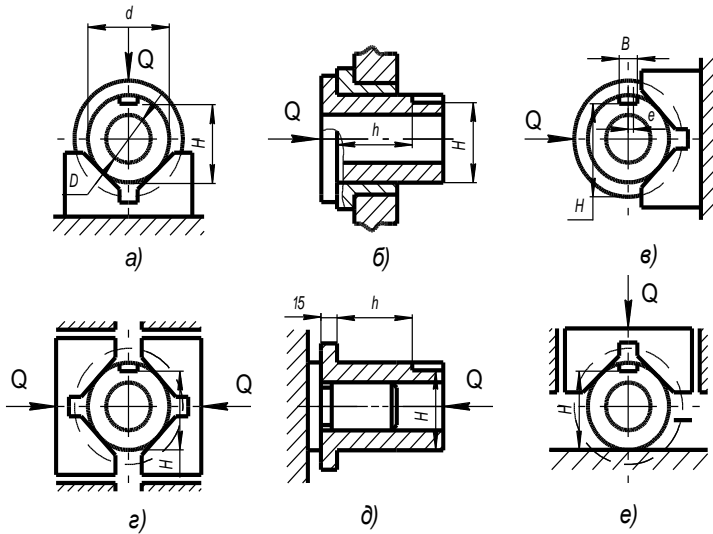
Схеми встановлення заготовки при обробці шпонкового пазу (до задачі 7).
